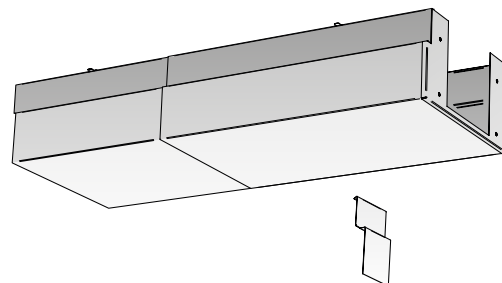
Zubehör – Anschlussabdeckung inkl. zugehöriges Abdeckblech, um die Öffnung voll abzudecken.
